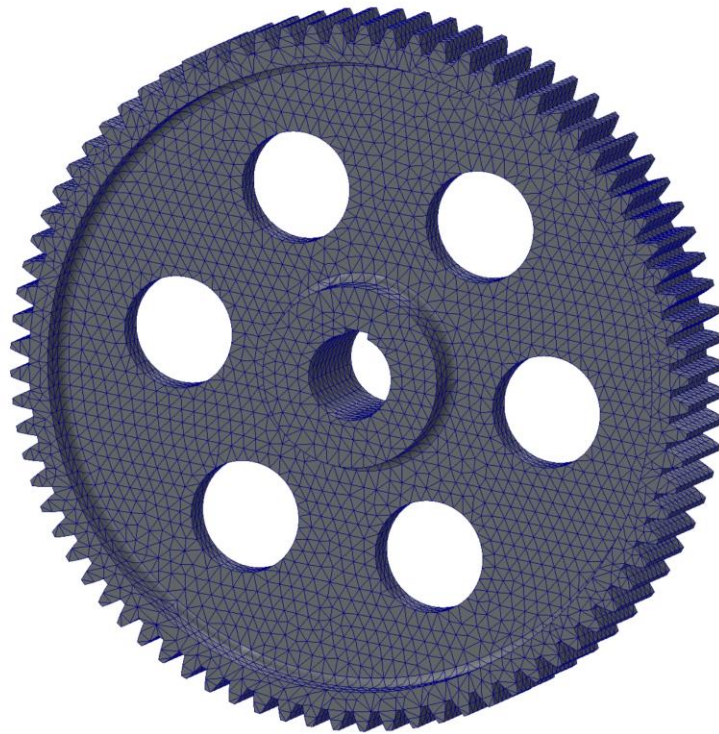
Розрахункова сітка шестерні вузла приводу фаршмішалки
